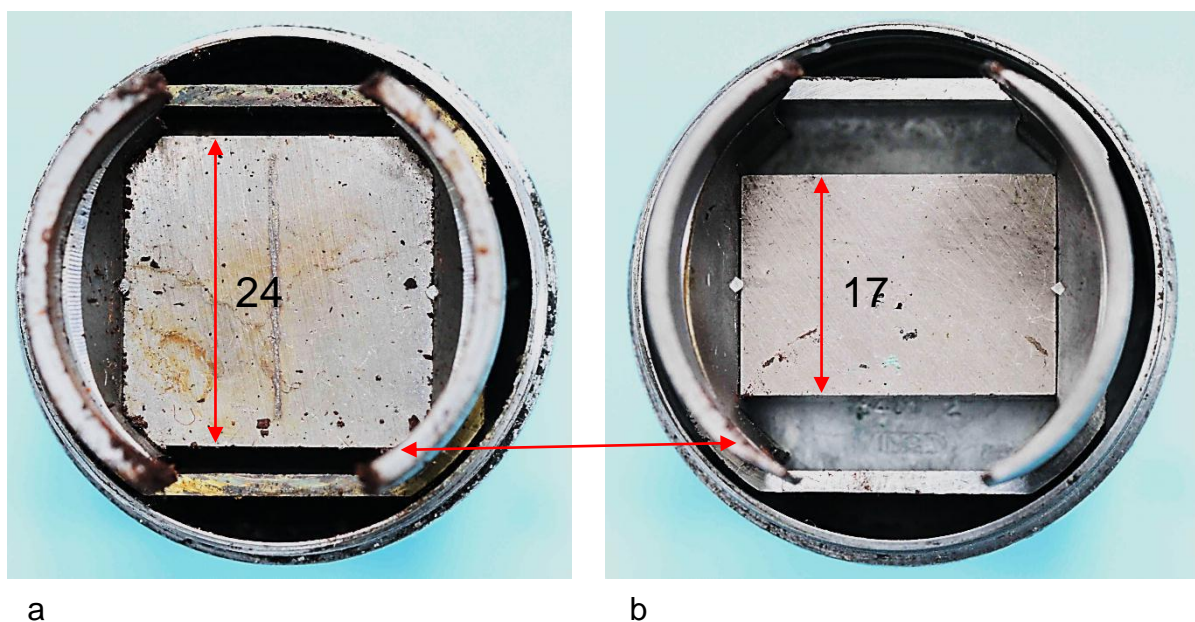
Magnetabmessungen: a) Lucifer Baby C 321139, b) Lucifer Baby 700 F 305 718
